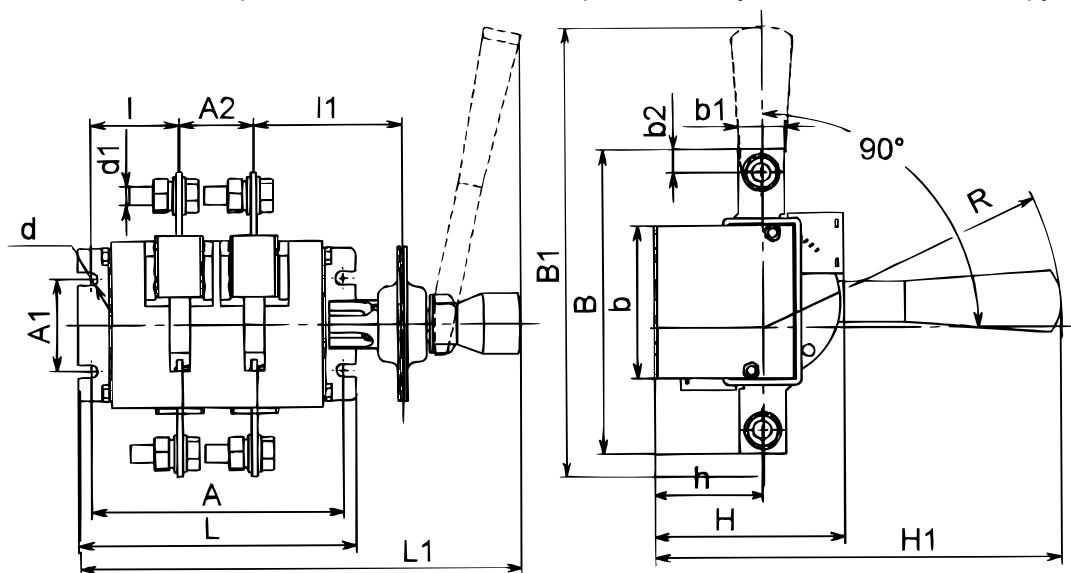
Выключатель-разъединитель на одно направление двухполюсный с боковой смещенной рукояткой
